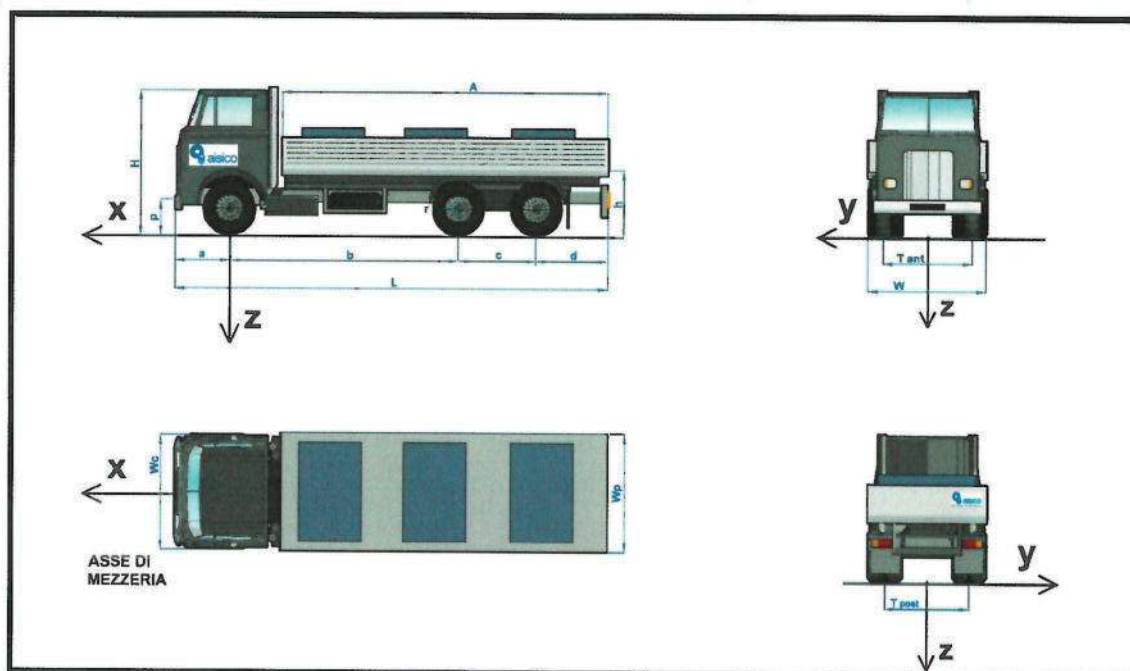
Figure 3 Dimensioni del veicolo – Vehicle dimensions
